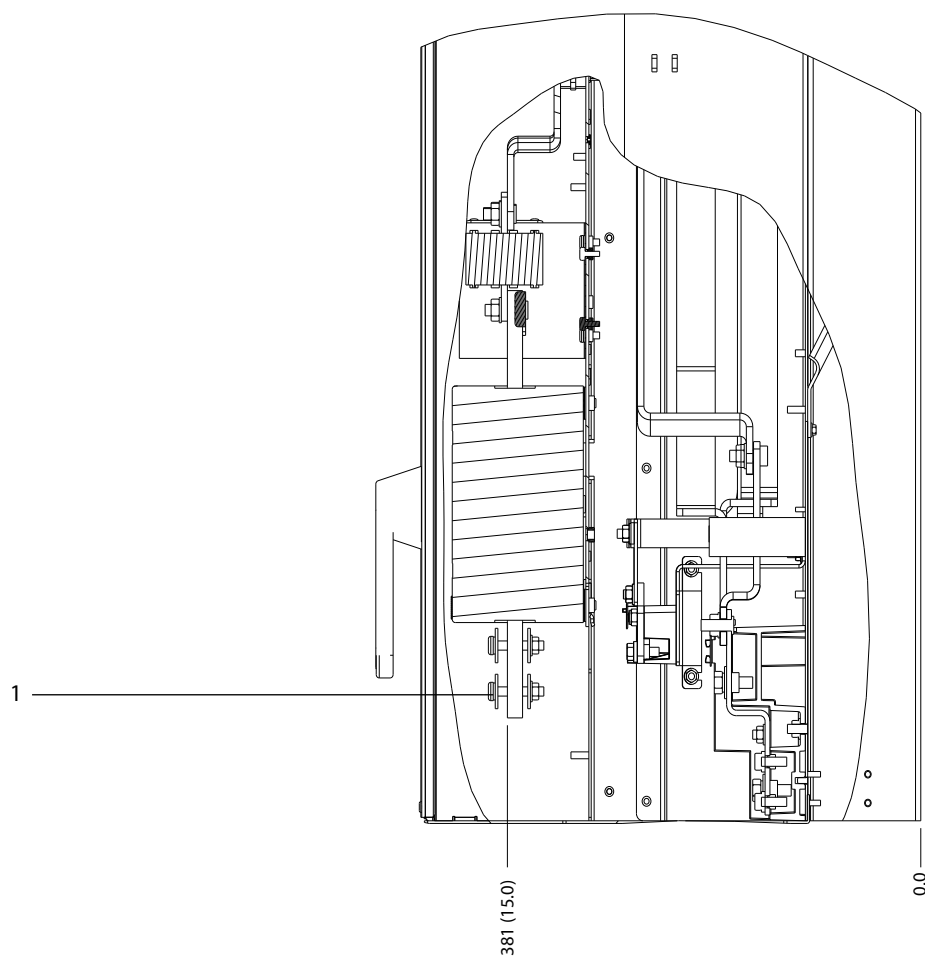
Dimensions de la borne des boîtiers E2, vue latérale
